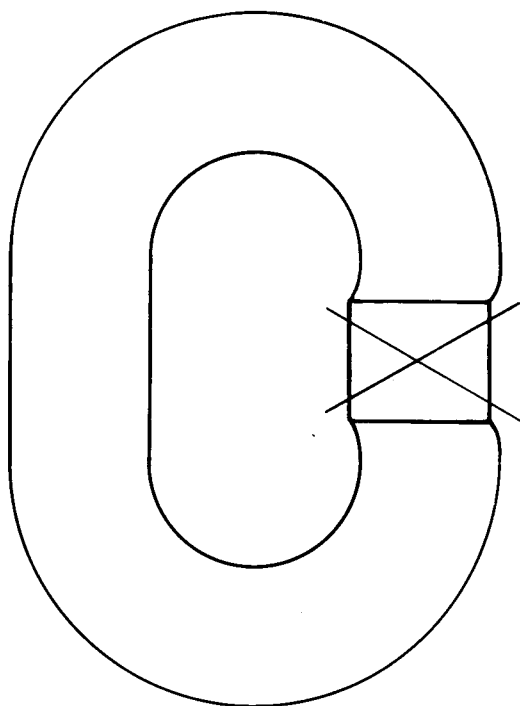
Creux à la soudure (non autorisé)
